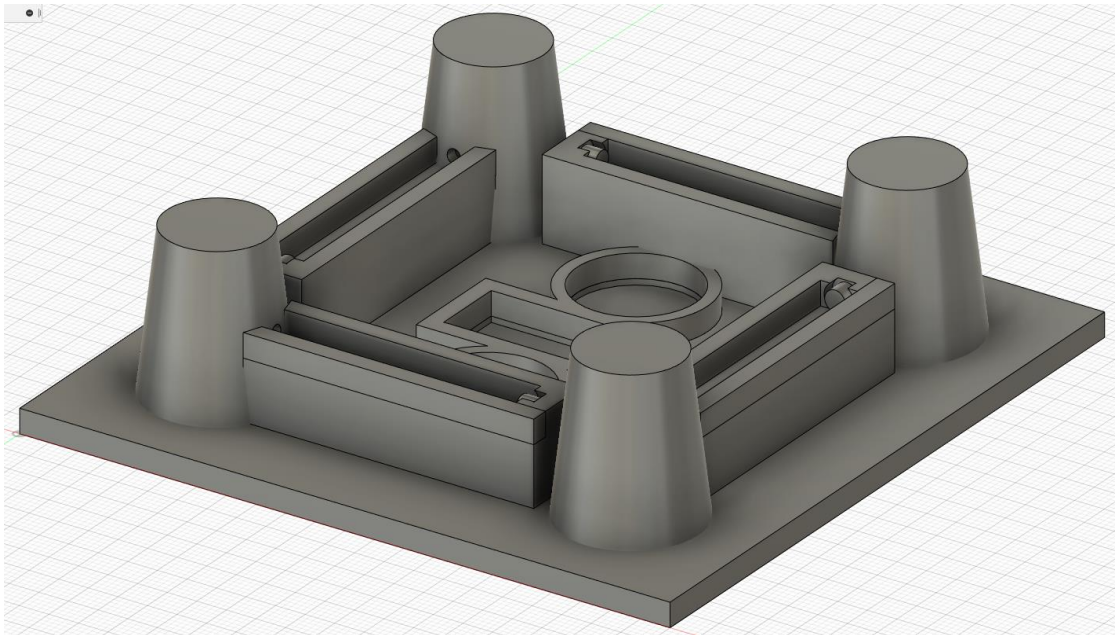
Базова поверхня з конусами та додатковими корпусами під стопорний штифт
